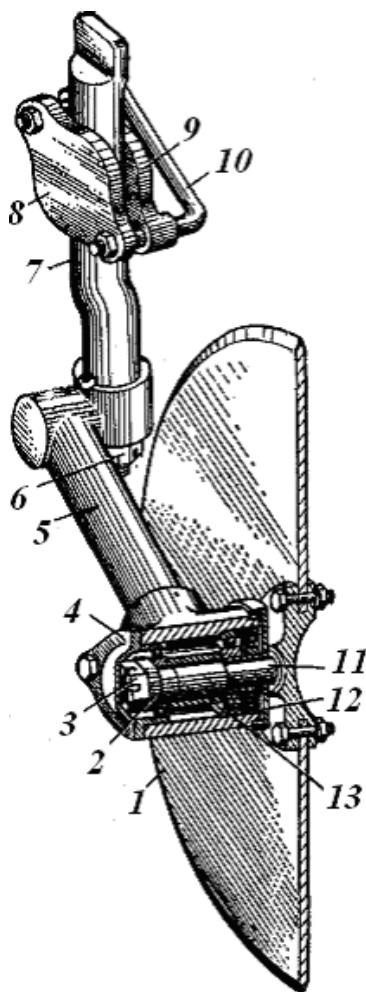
Дисковий ніж: 1 - диск; 2 - шайба; 3 - гайка; 4 - ковпак; 5 - консоль; 6 - корончата шайба; 7 - стояк; 8 - накладка; 9 - підкладки; 10 - хомут; 11 - вісь; 12 - ущільнення; 13 - шарикопідшипник
